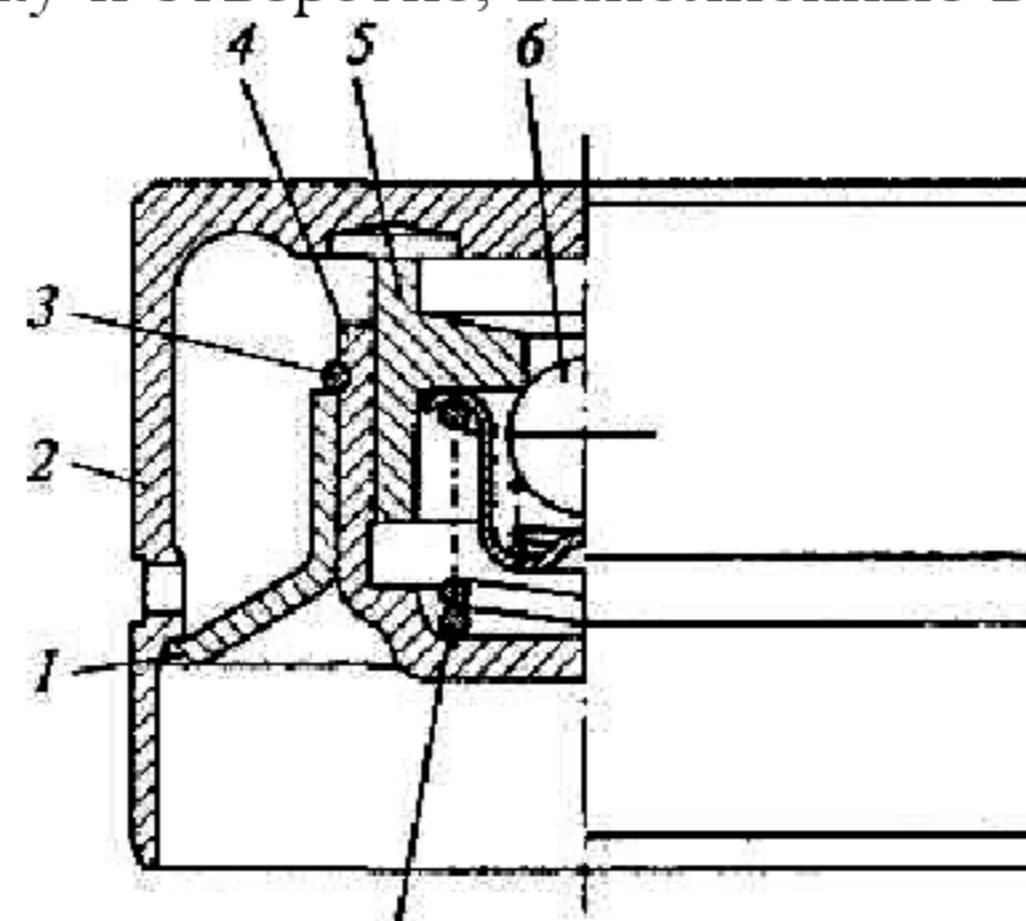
Гидравлический толкатель: 1 — втулка; 2, 4 — корпуса; 3 — кольцо; 5 — поршень; 6 — клапан; 7 — пружина
